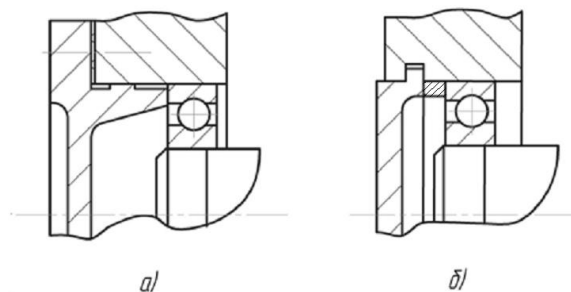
Види підшипникових кришок циліндричних редукторів
